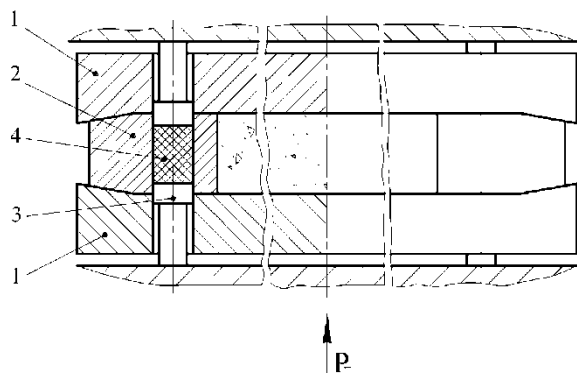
Одноместная пресс-форма для прессования графитопластовых вставок токоъемников: 1 – боковина; 2 – торцевая пластина; 3 – штифт; 4 – упругий элемент [4]
